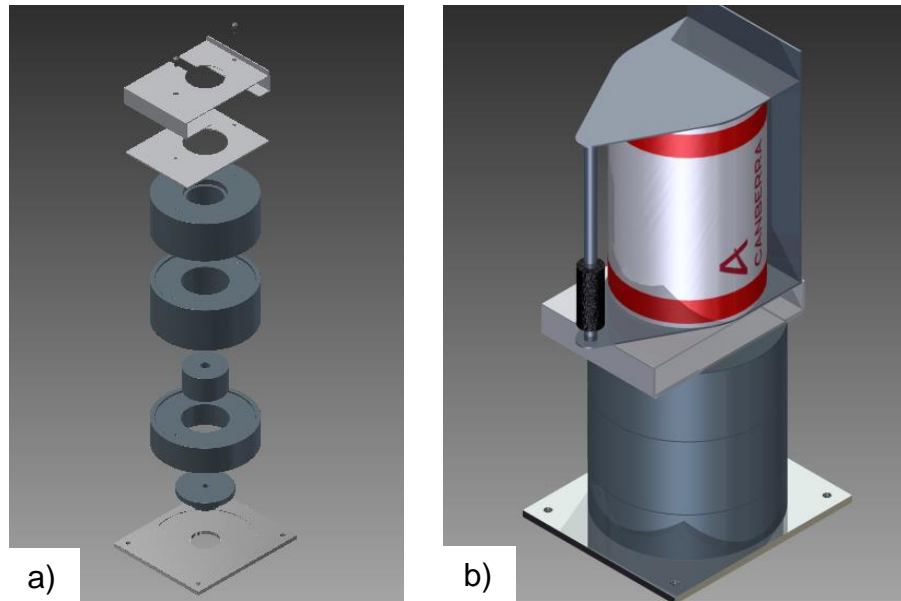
a) Despiece de torre anular y piezas de acople del detector respecto a base en que va montada. b) Detector en posición dentro de su blindaje.
